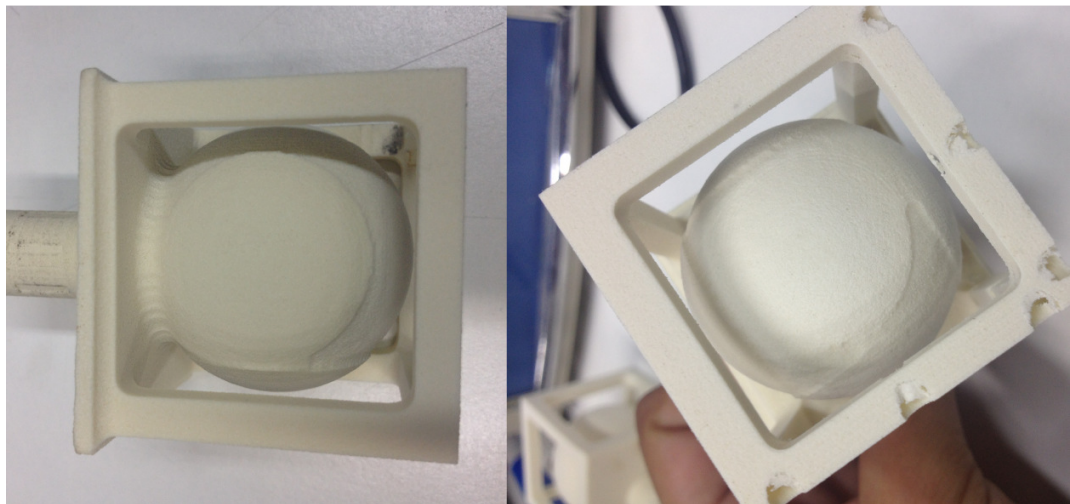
Defeito de usinagem devido a problema de referenciamento
